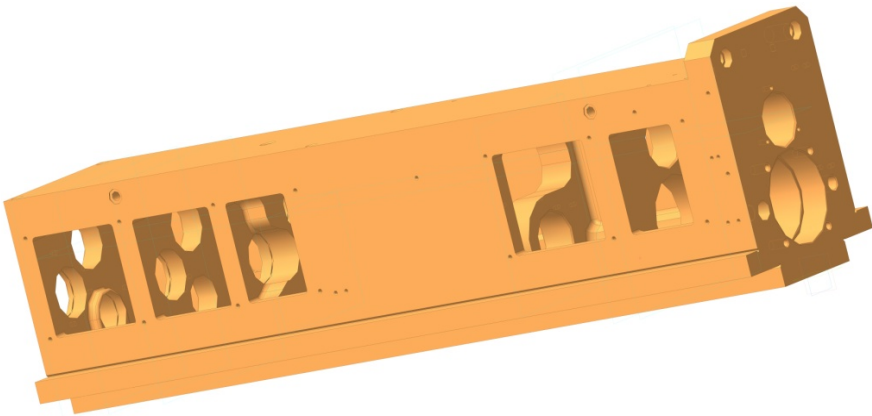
3D-модель корпусу горизонтальної шпиндельної бабки
